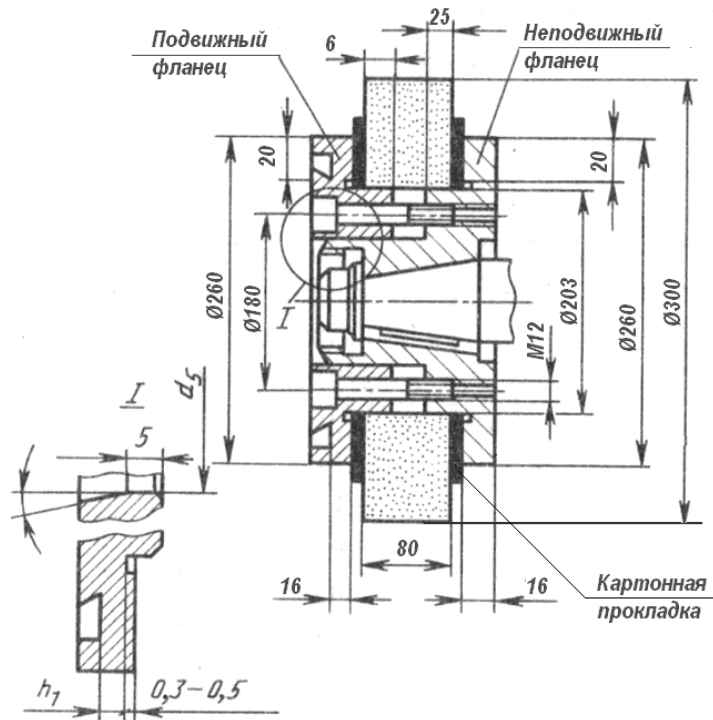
Крепление абразивного круга на планшайбе
